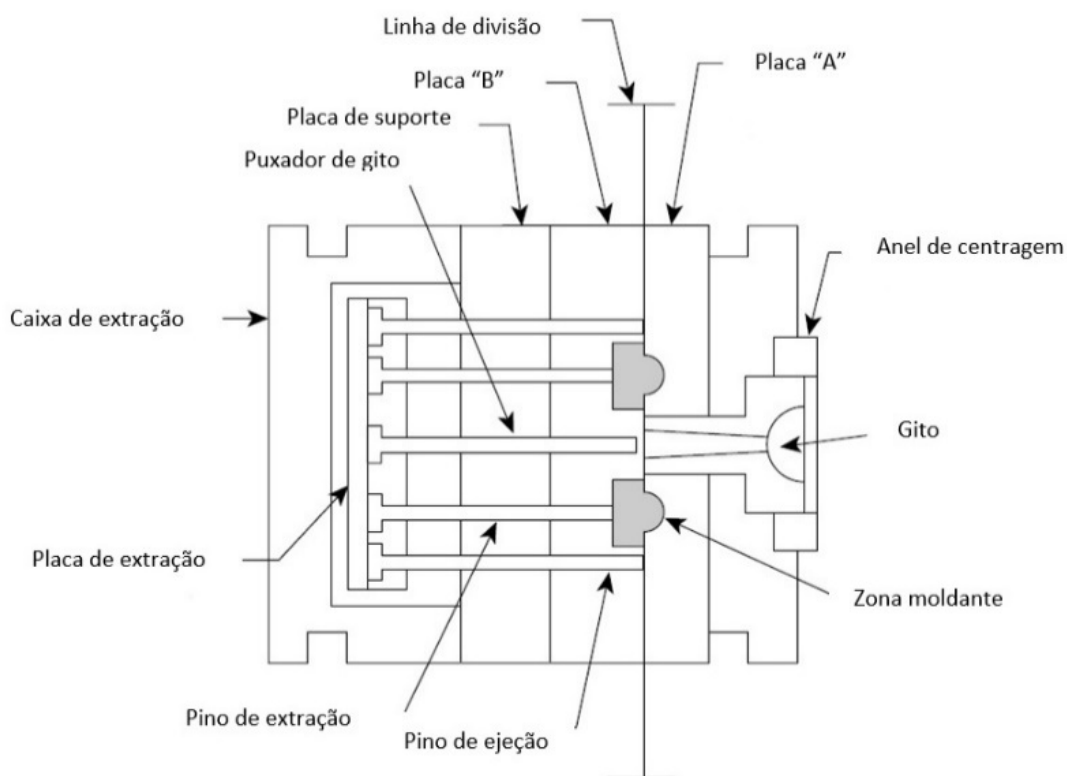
Componentes básicos internos de um molde de duas placas [8].
